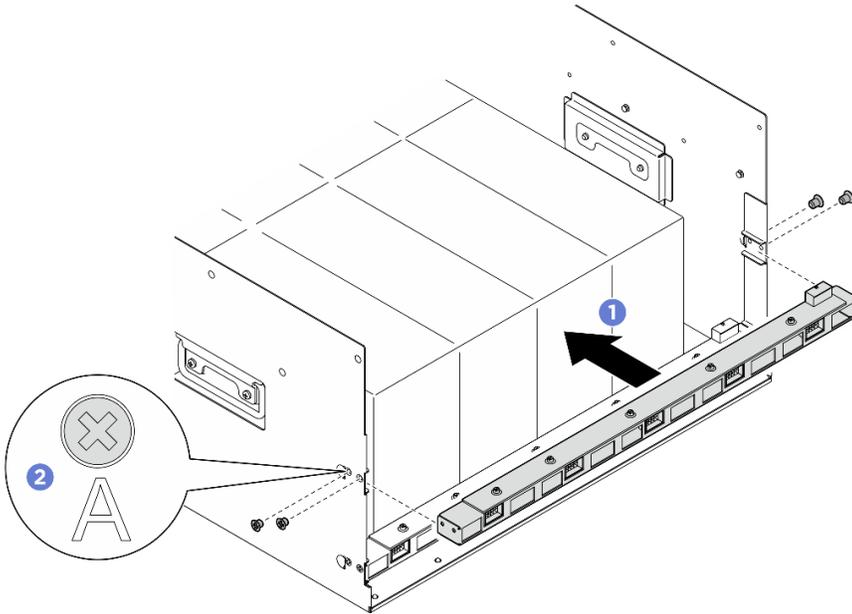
Instalación del conjunto de la placa de control del ventilador posterior
